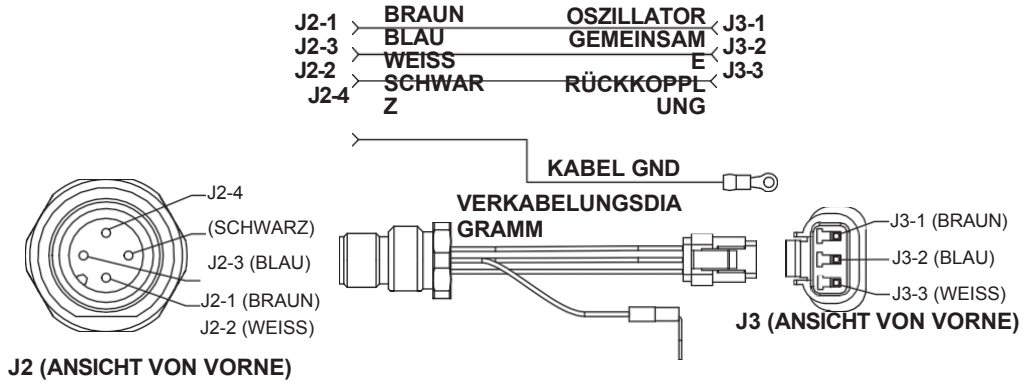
Kabelbaum der Pistolensteckdose
